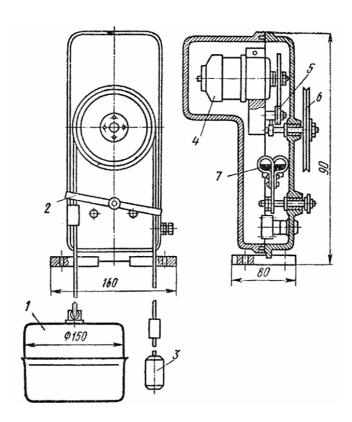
Поплавковый уровнемер РП-1065: 1 – поплавок; 2 – коромысло; 3 – противовес; 4 – сельсин-датчик; 5 – механическая передача; 6 – шкив; 7 – ртутные контакты
